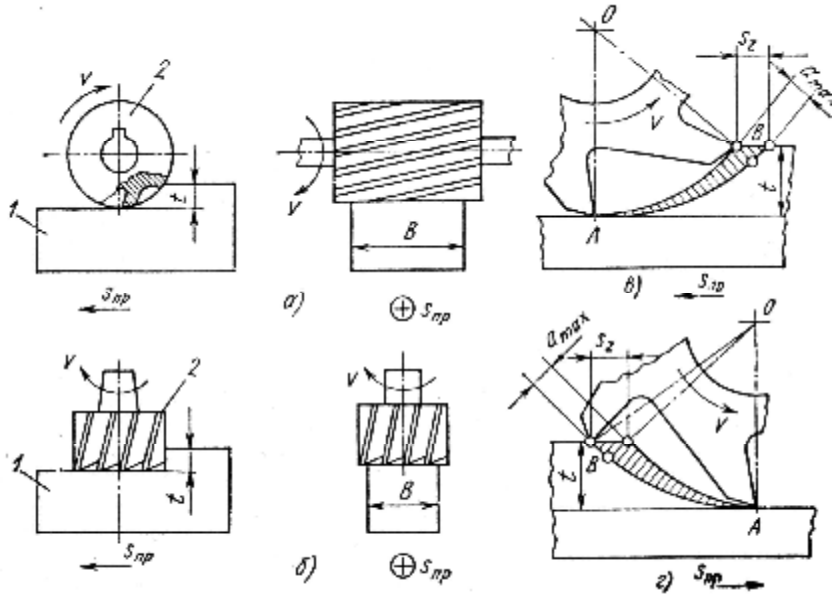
Схемы фрезерования цилиндрической (а) и торцевой (б) фрезой, встречного (в) и попутного (г) фрезерования:
